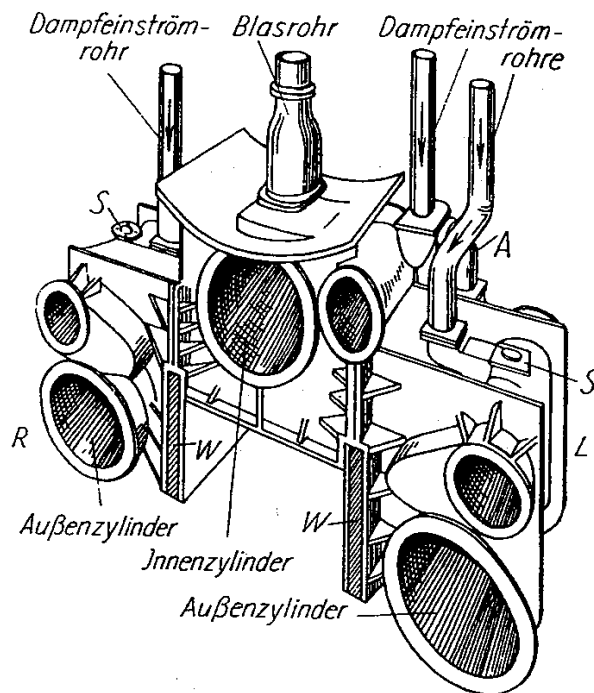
Zylinderanordnung einer Zwillingsdampfmaschine
